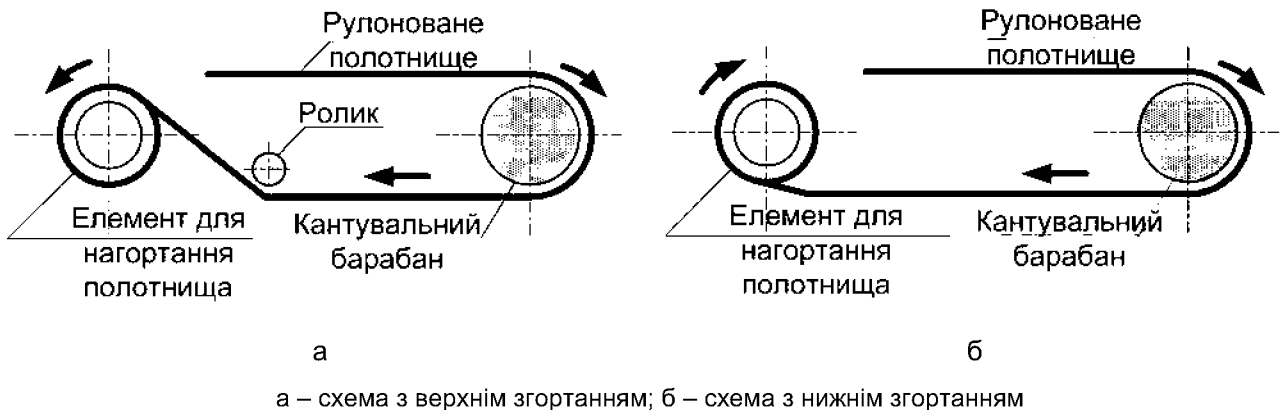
Схема установки для згортання полотнищ резервуарних конструкцій
